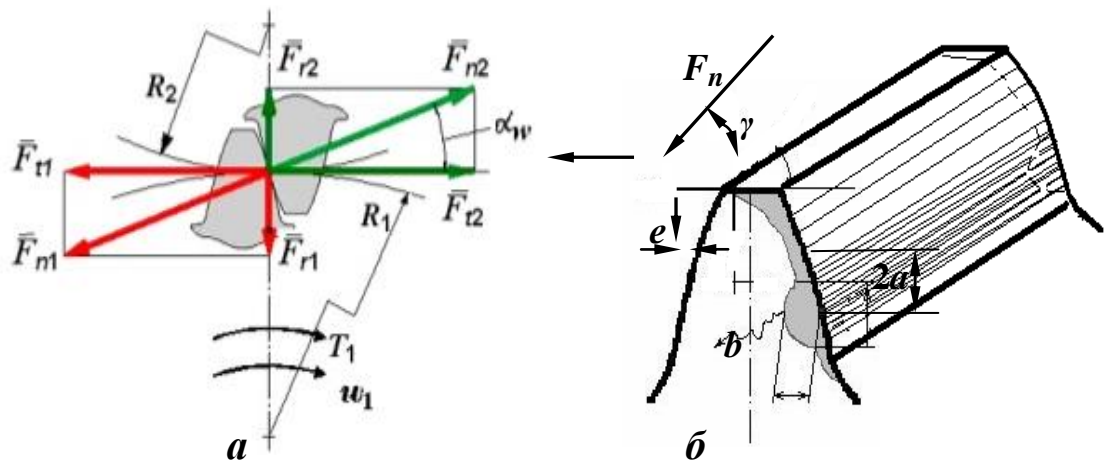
Сили зачеплення в циліндричній зубчастій передачі (а);
